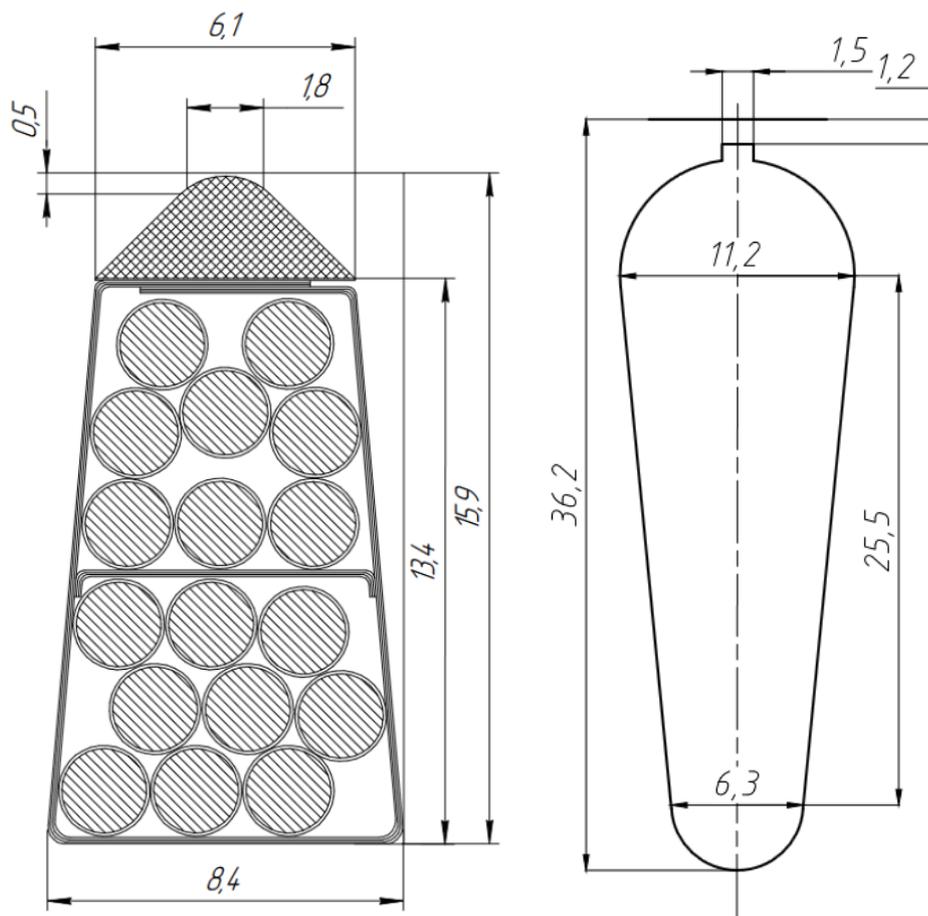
Примеры чертежей пазов статора (слева) и ротора (справа)
